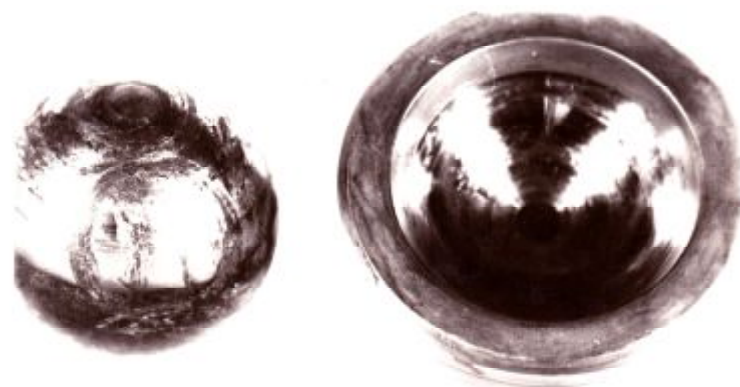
Внешний вид рабочей поверхности шара и обоймы после приработки
